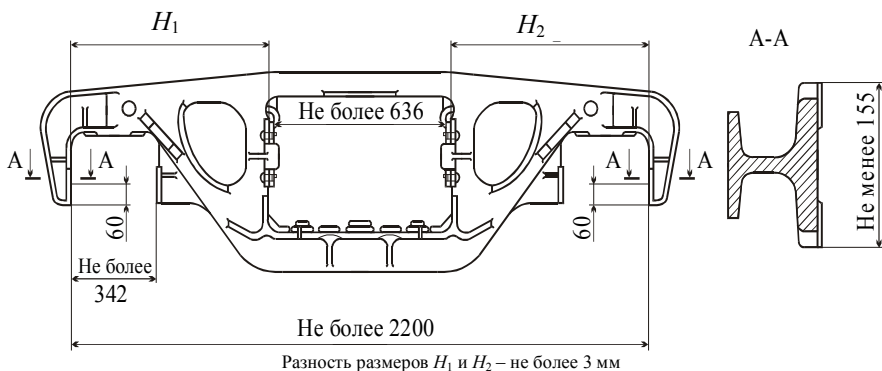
Размеры боковых рам грузовых тележек модели 18-100 при выпуске из капитального ремонта
